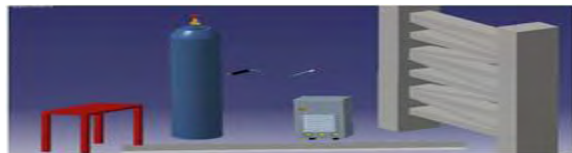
Herramientas y utensilios de trabajo del soldador. Fuente: CATIA.
